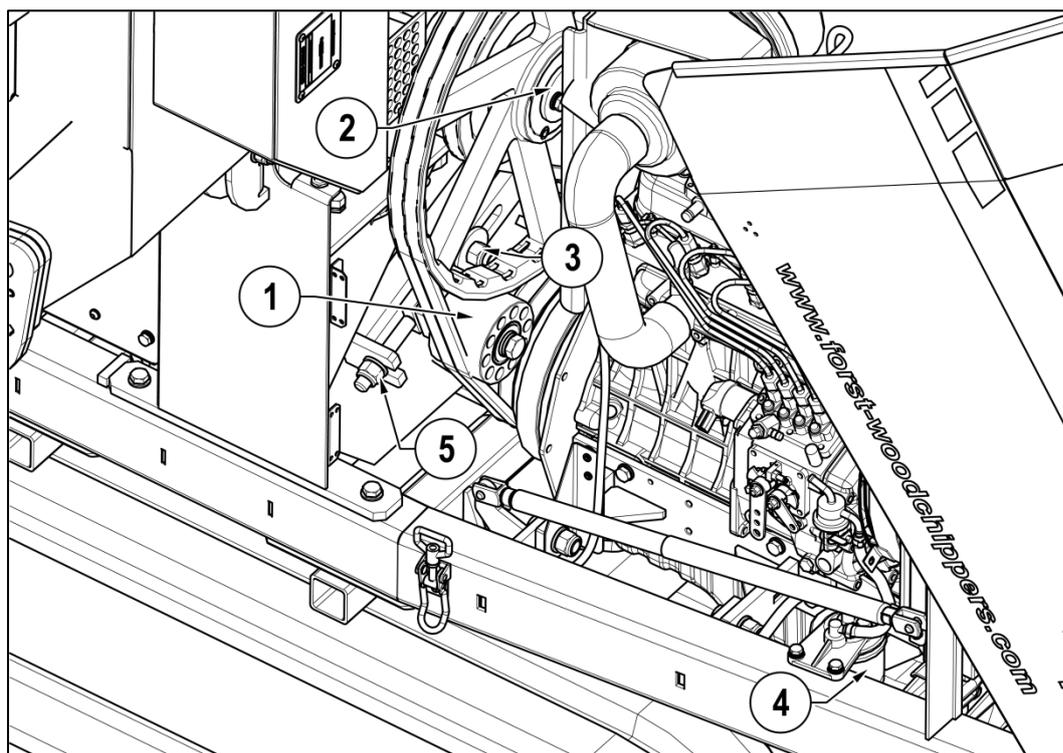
UMLENKROLLE, SCHWUNGRAD-RIEMENSPELLER
